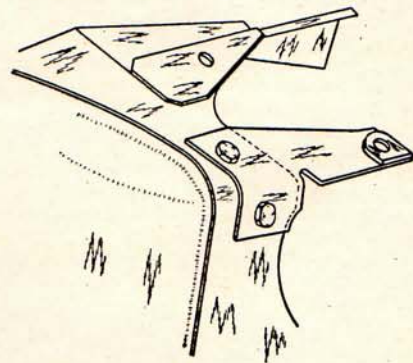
Fixation du collecteur d'air (nouveau montage).
